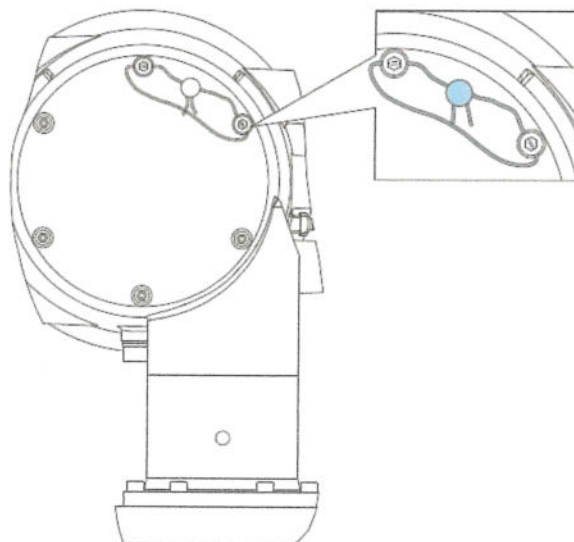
mechanische Versiegelung der Gehäuserückseite
